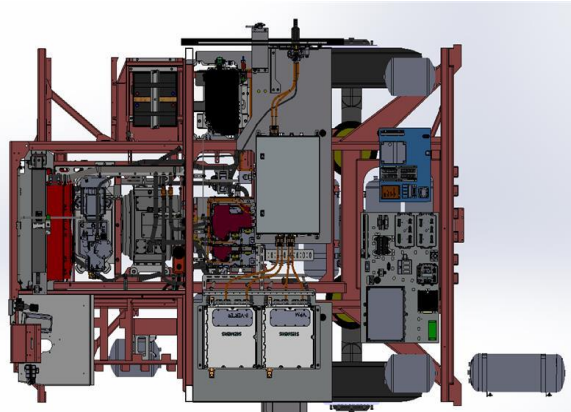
Vista 3D (superior) do chassis e.Cobus
